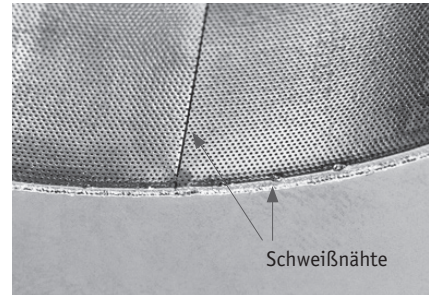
Filterrohr mit Schweißnaht und angeschweißtem Flansch
